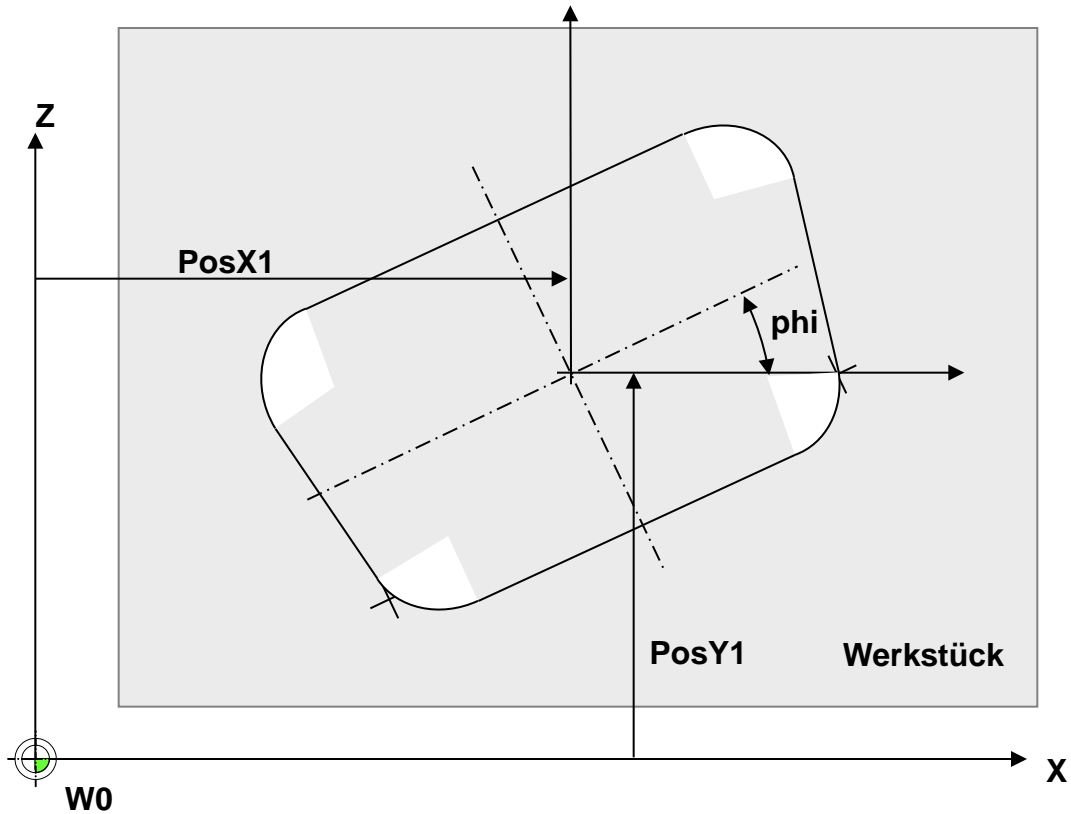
Parameter für die Definition einer rechteckigen Frästasche
